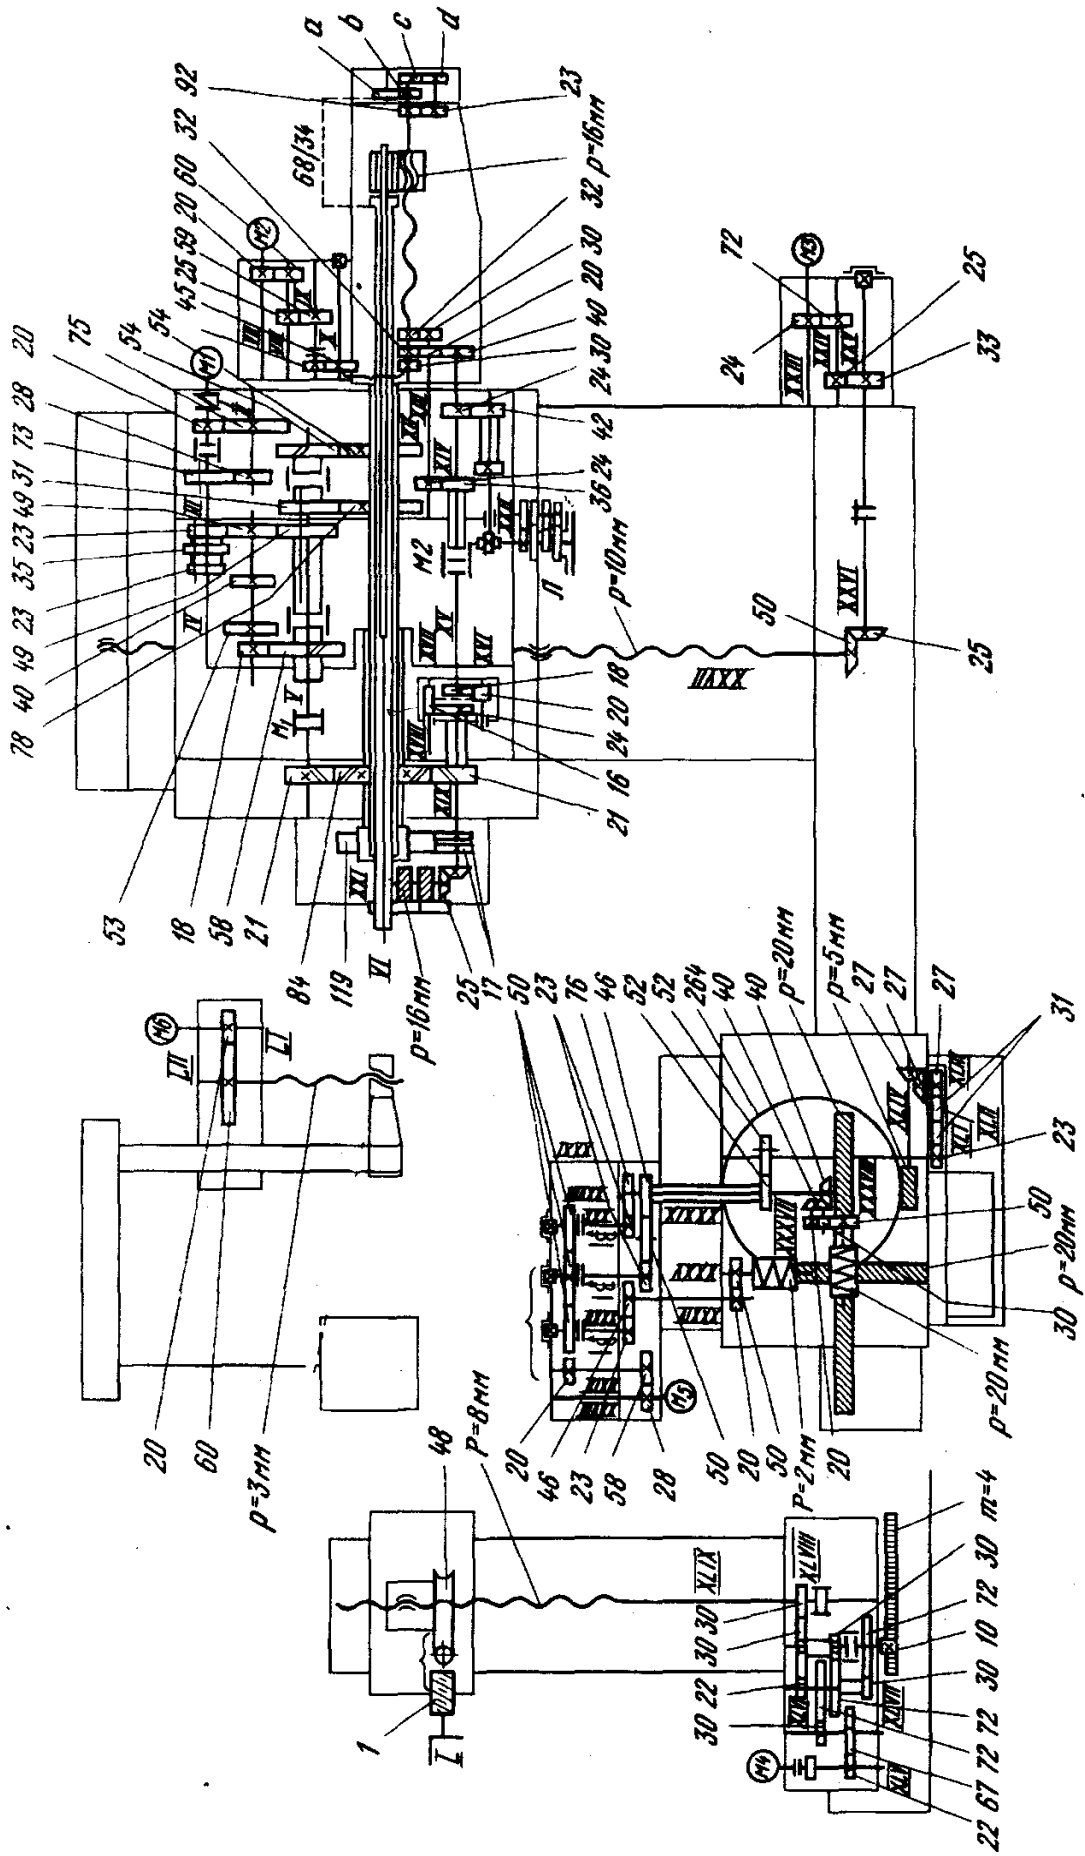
Кинематическая схема станка модели 2П636ГФ1
